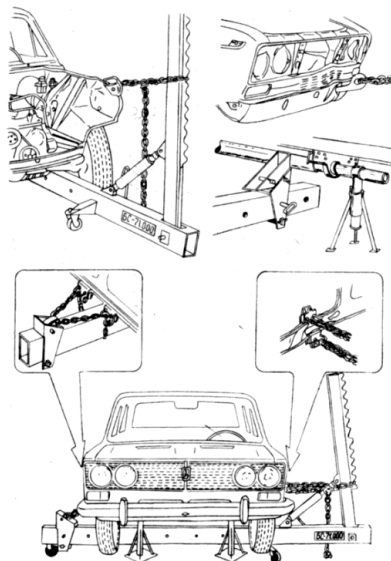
Закрепление устройства БС-71.000 при правке кузова
